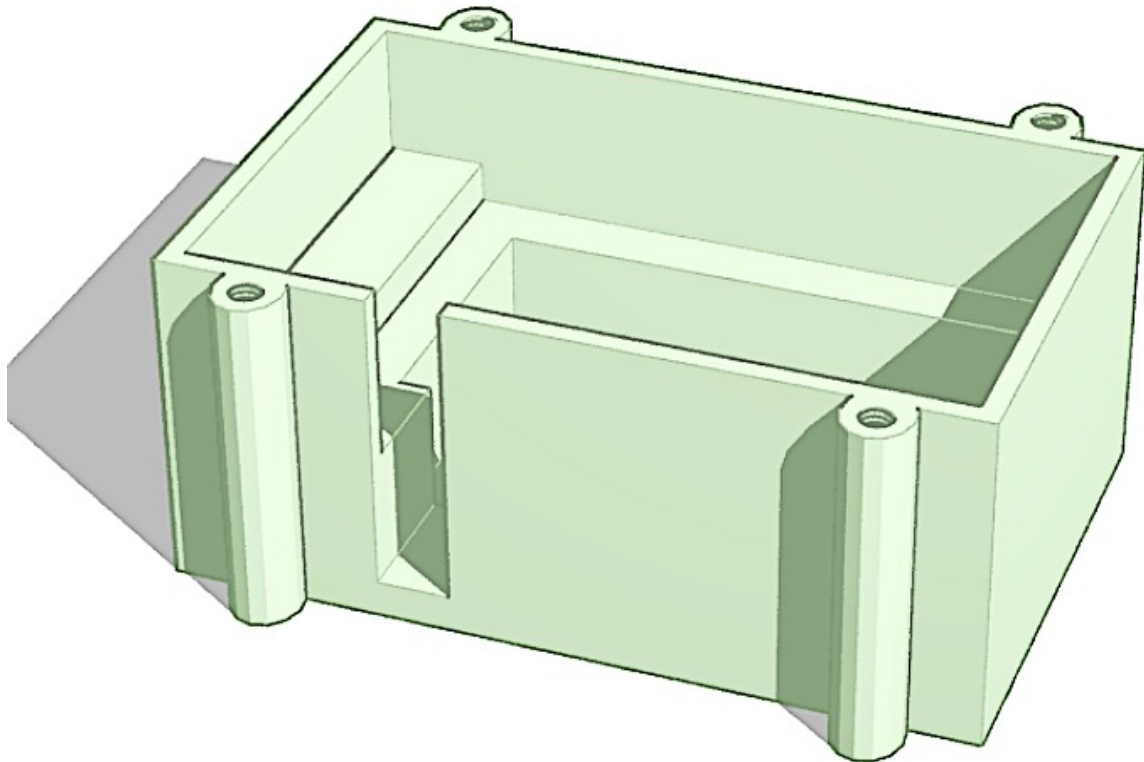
Diseño de encapsulado sin tapa para impresión en 3D. Base diseñada en una pieza que nunca llegó a ser impresa.
